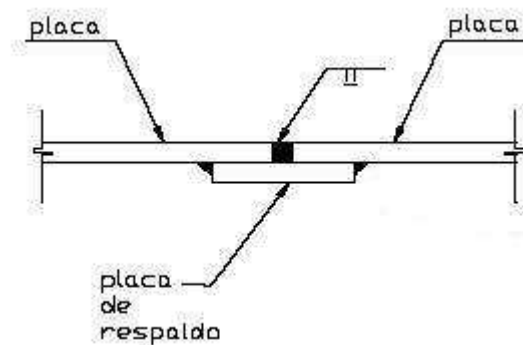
Soldadura a tope simple con respaldo.
